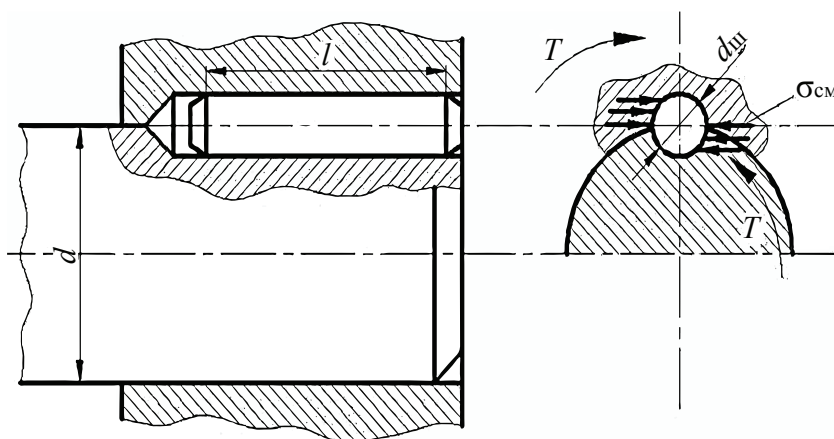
Соединение деталей цилиндрической шпонкой
